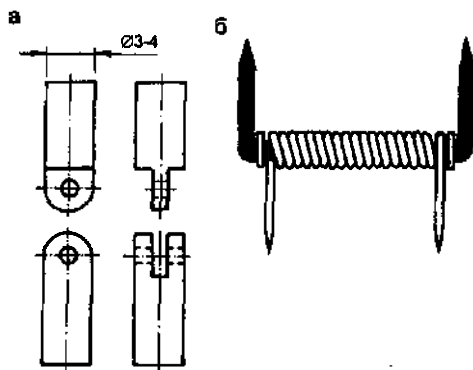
Шарнирные петли для шкатулки: а — из стального стержня; б — из проволоки
